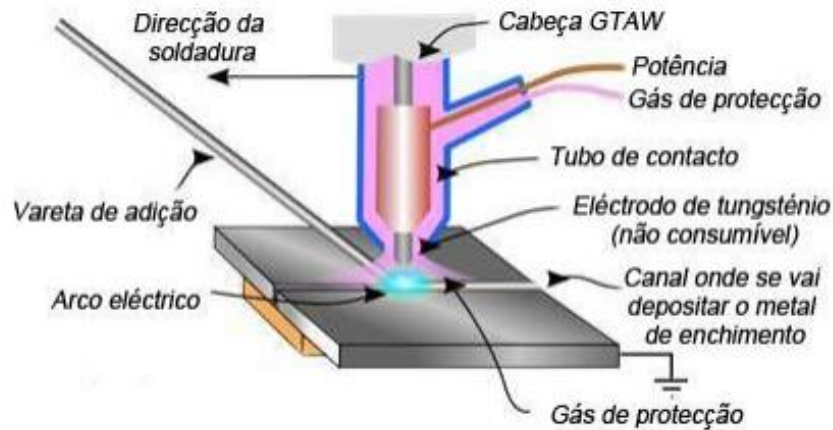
Princípio de funcionamento da soldadura TIG [44]
